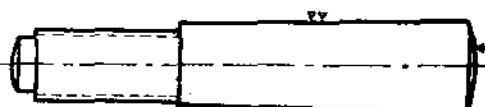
Болт конусный для отверстий из-под развертки (призанный).
